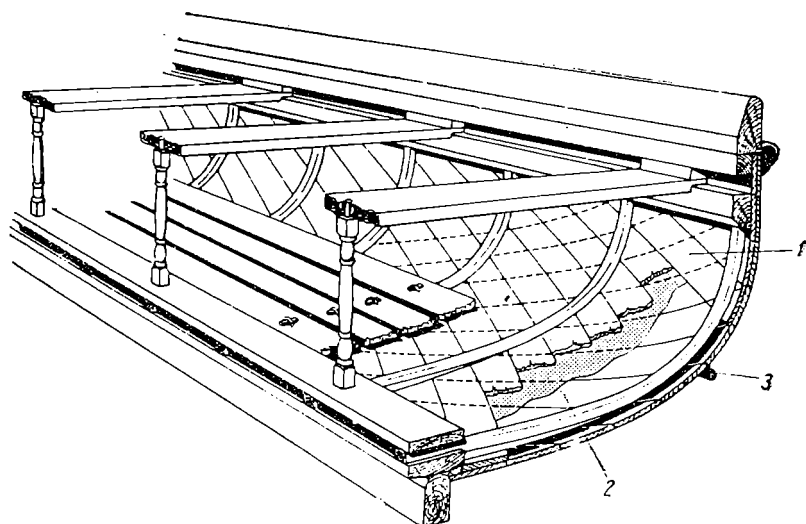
Detalii la o barcă construită în sistem diagonal:
